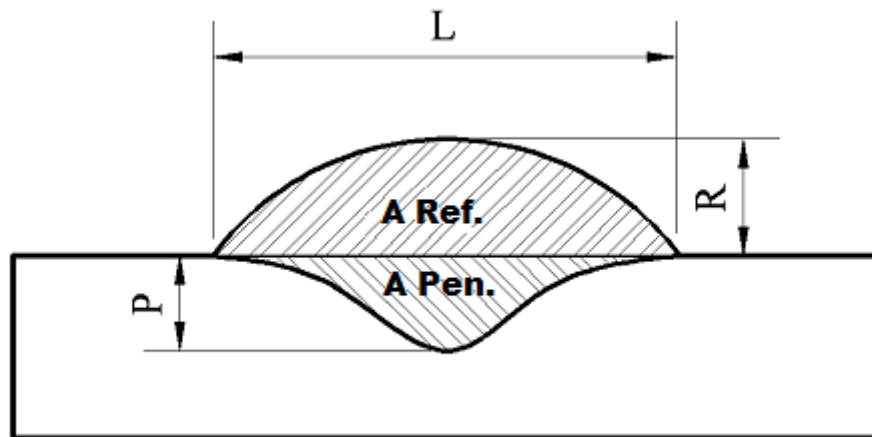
Representação das dimensões geométricas das seções transversais dos cordões de solda
